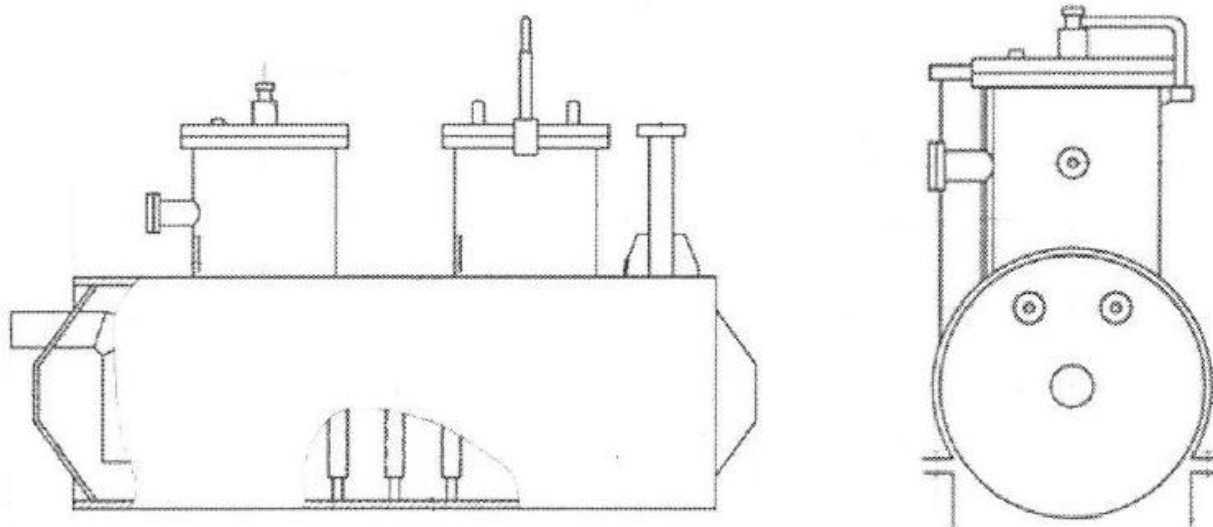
Общий вид резервуара ЕП-25-2400-1-3
